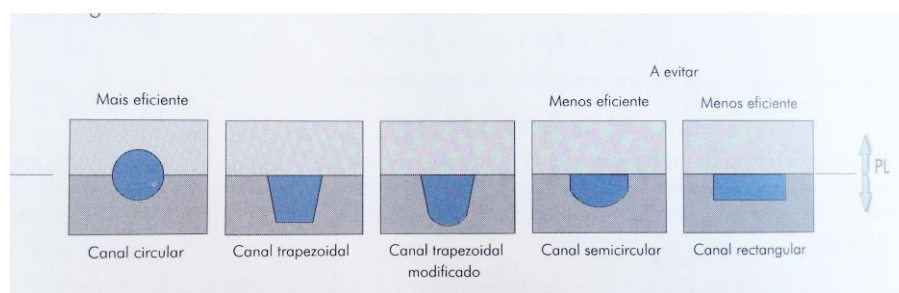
Geometrias utilizadas nos canais de injeção [1]
